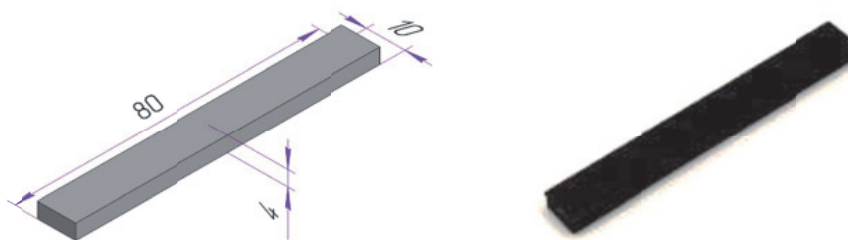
3D модель и распечатанный образец (брусок)
